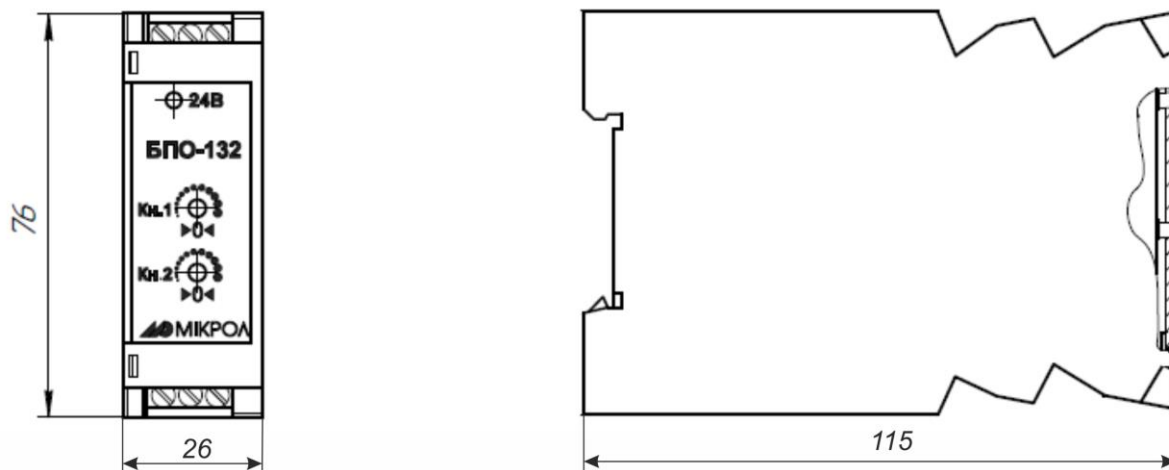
Зовнішній вигляд і габаритні розміри БПО-132
